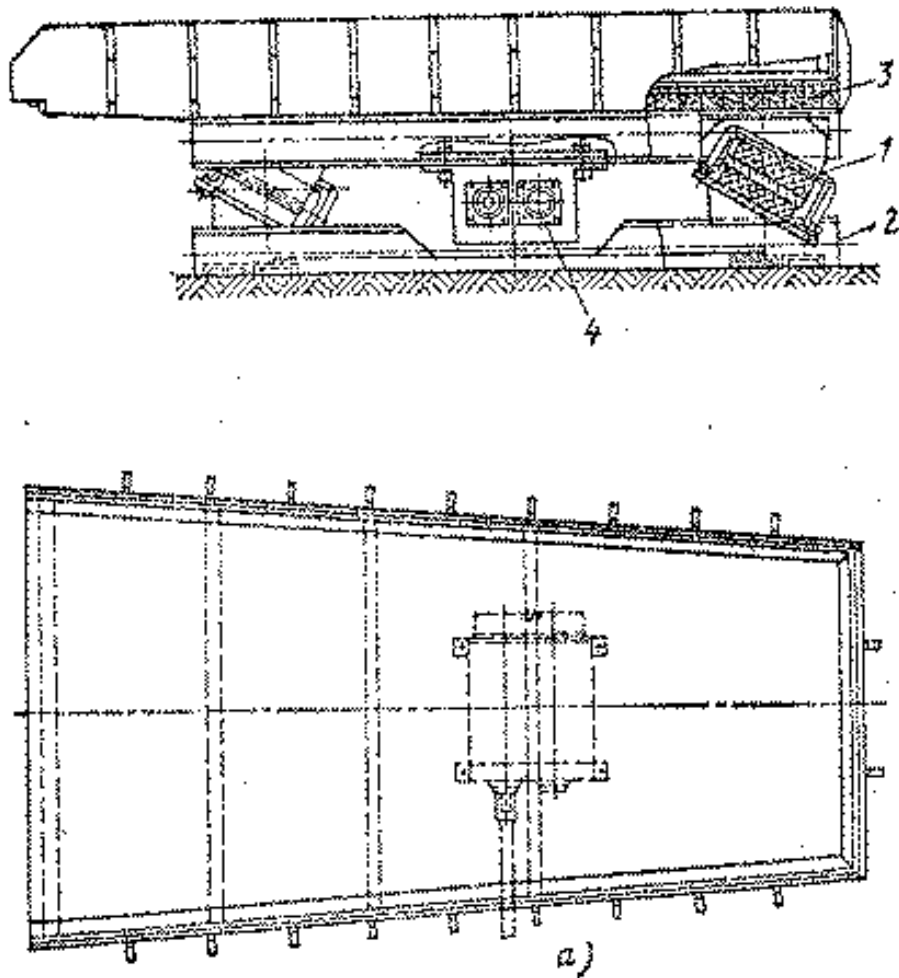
Принципова схема віброживильника активного типу:
